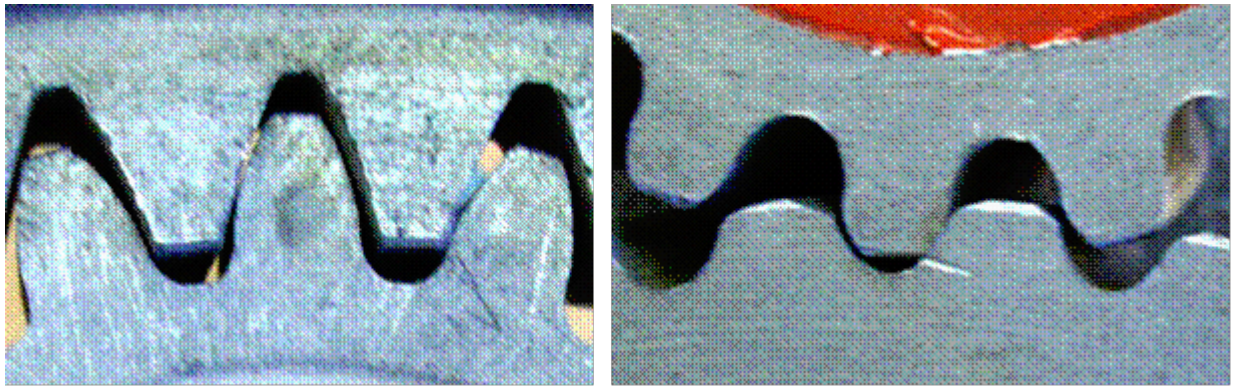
Виды зубчатых колес: с эвольвентным профилем зубьев (слева), зубчатые колеса передачи Новикова
